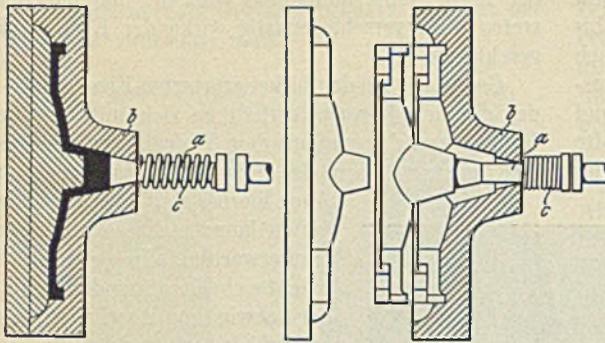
Ausstoßvorrichtung für Gußstücke.
